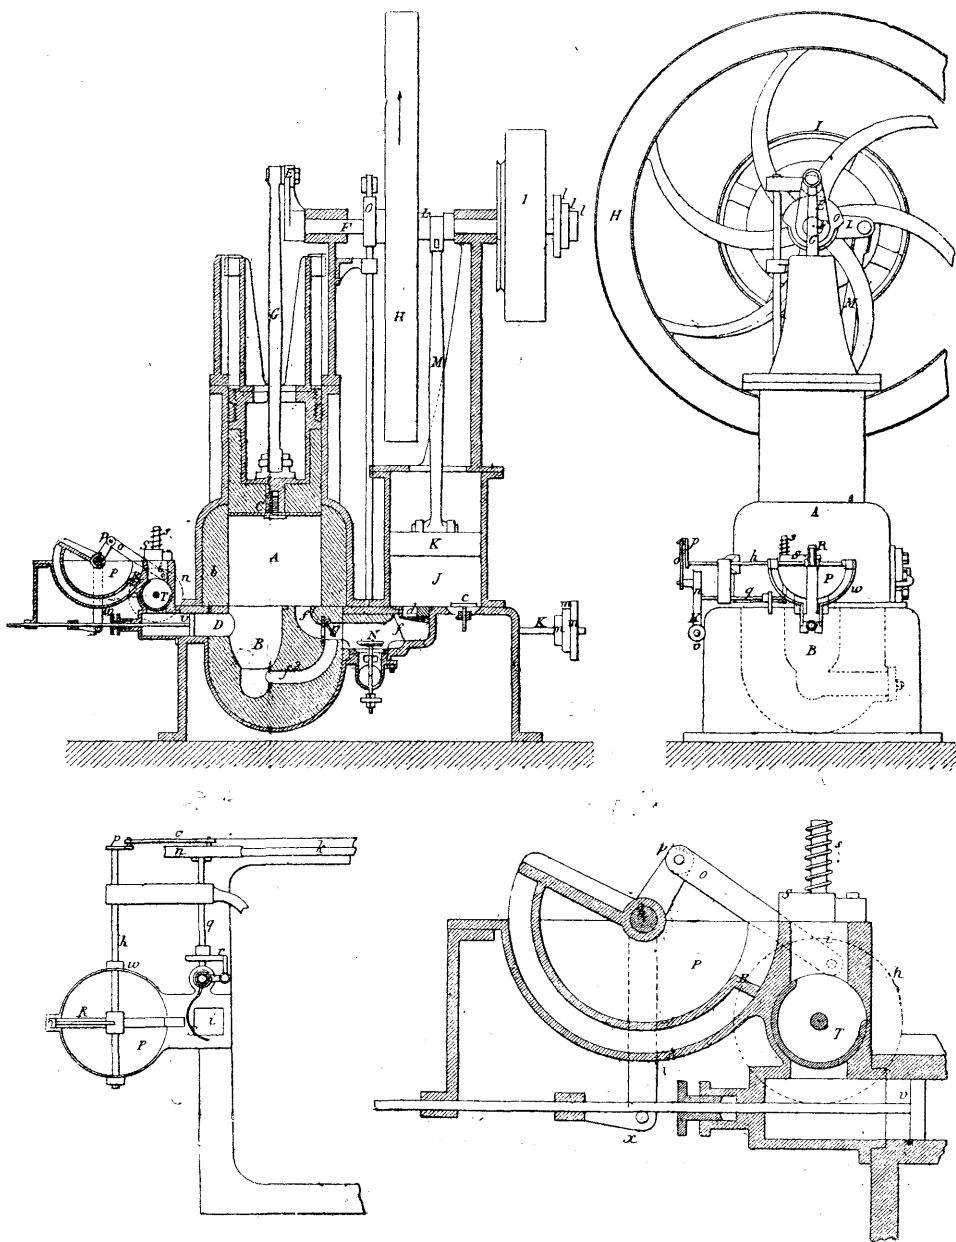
à 70. — *Machine Leavitt*. — Coupe verticale par le cylindre moteur, vue par bout, plan et détail du chargeur.
